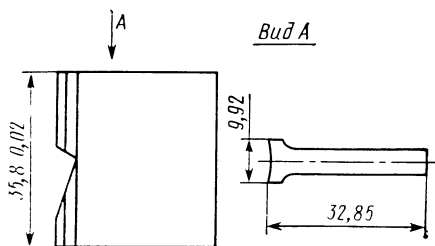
Секция твердосплавной матрицы штампа ШТ-600
